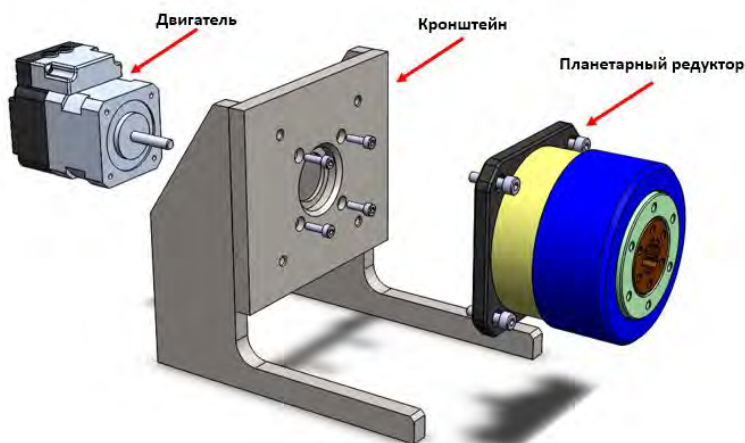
Механическая конструкция: двигатель – кронштейн - редуктор.
